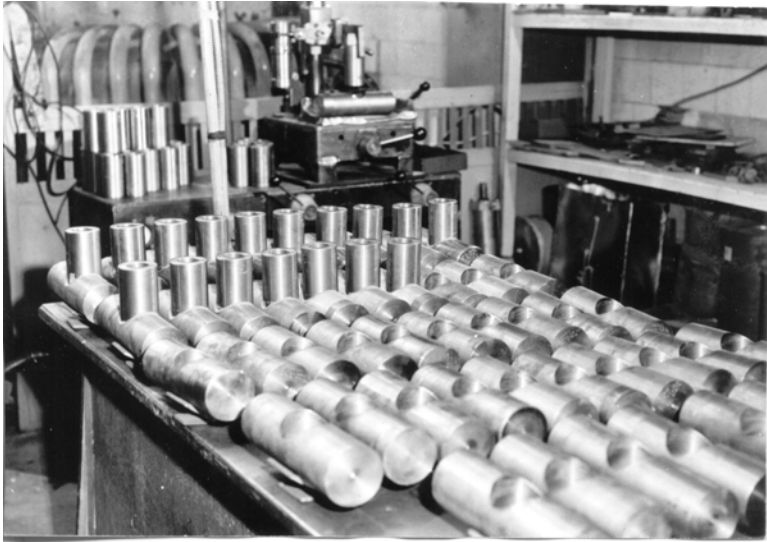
Стенд для складання деталей заготовок трійників під паяння із широким зазором
